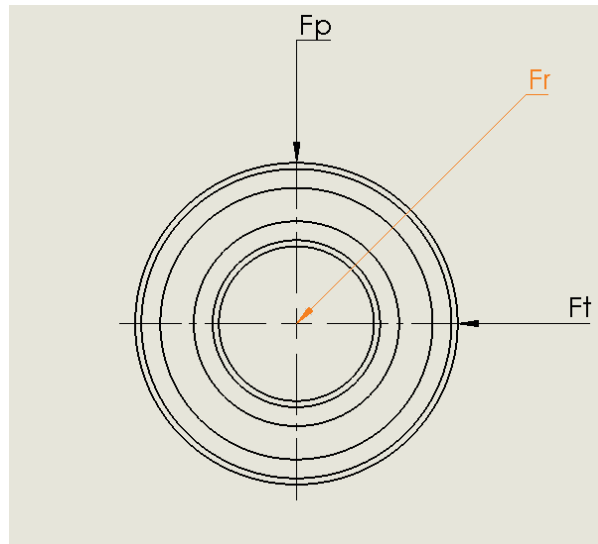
Composición de cargas actuantes sobre rodamiento.
